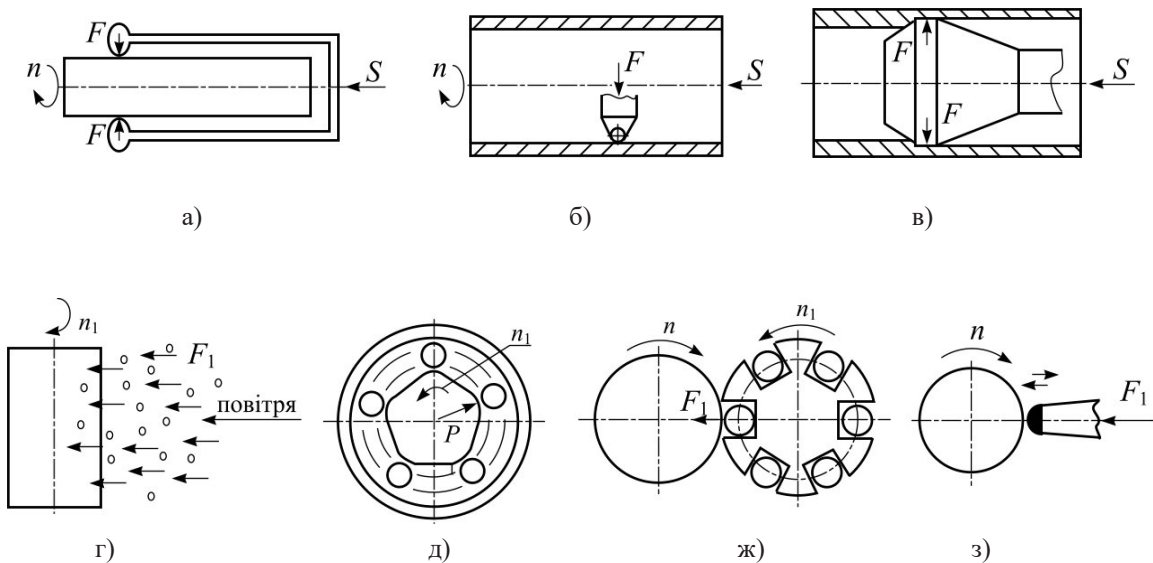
Способи поверхневого пластичного деформування (зміцнення) деталей статичні (а – обкочування; б – вигладжування; в – дорнування) та динамічні (г – дробоструменева обробка; д – ударне розкочування; ж – відцентрова обробка; з – зміцнювальна чеканка)
